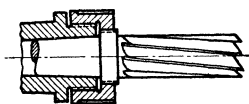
Fräserbefestigung mit Differentialgewinde.
